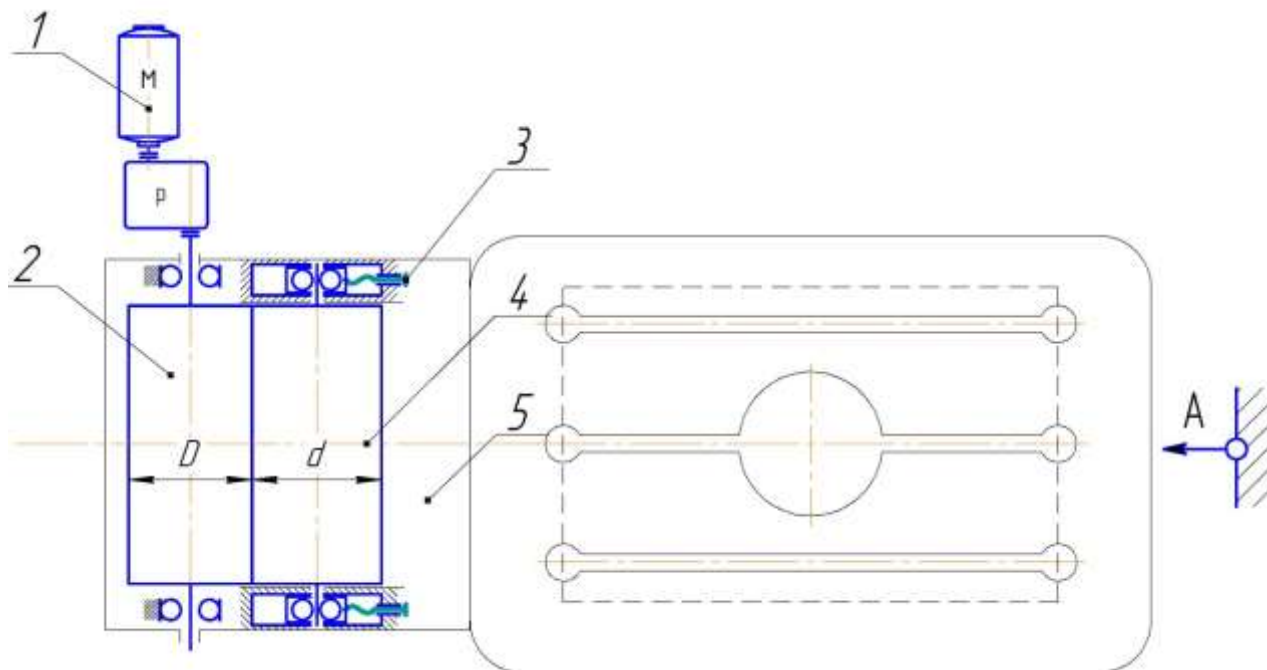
Кинематическая схема валковой подачи с индивидуальным приводом
